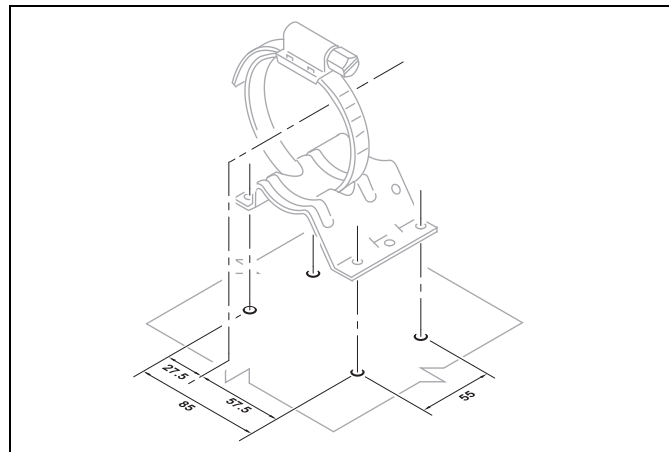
Схема расположения отверстий для установочного кольца циркуляционного насоса U 4814
